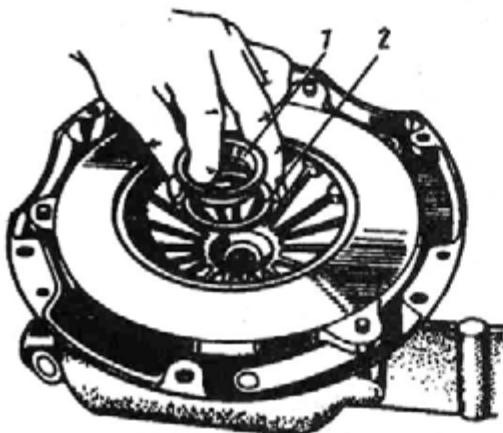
Установка центральной втулки крепления опорной пяты и пружинного кольца:
